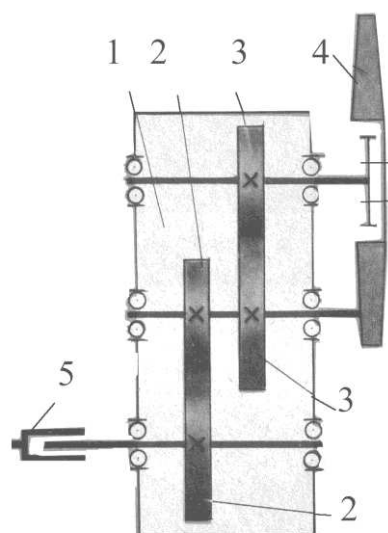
Кинематическая схема привода вентилятора: 1 – редуктор; 2, 3 – зубчатые колеса; 4 – лопастное колесо; 5 – карданный привод
